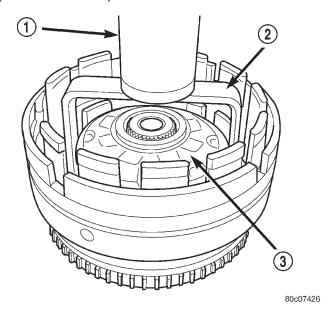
Compresión del émbolo regulador de baja y sobremarcha con la herramienta 8251
